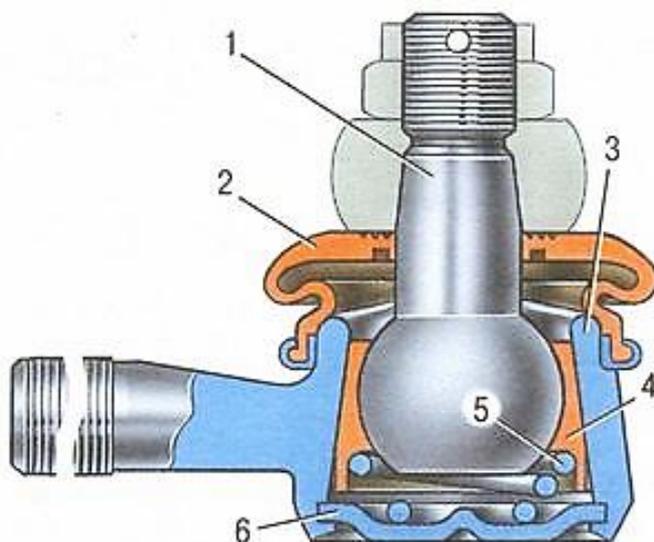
Шаровой шарнир рулевой тяги ВАЗ-2106:
